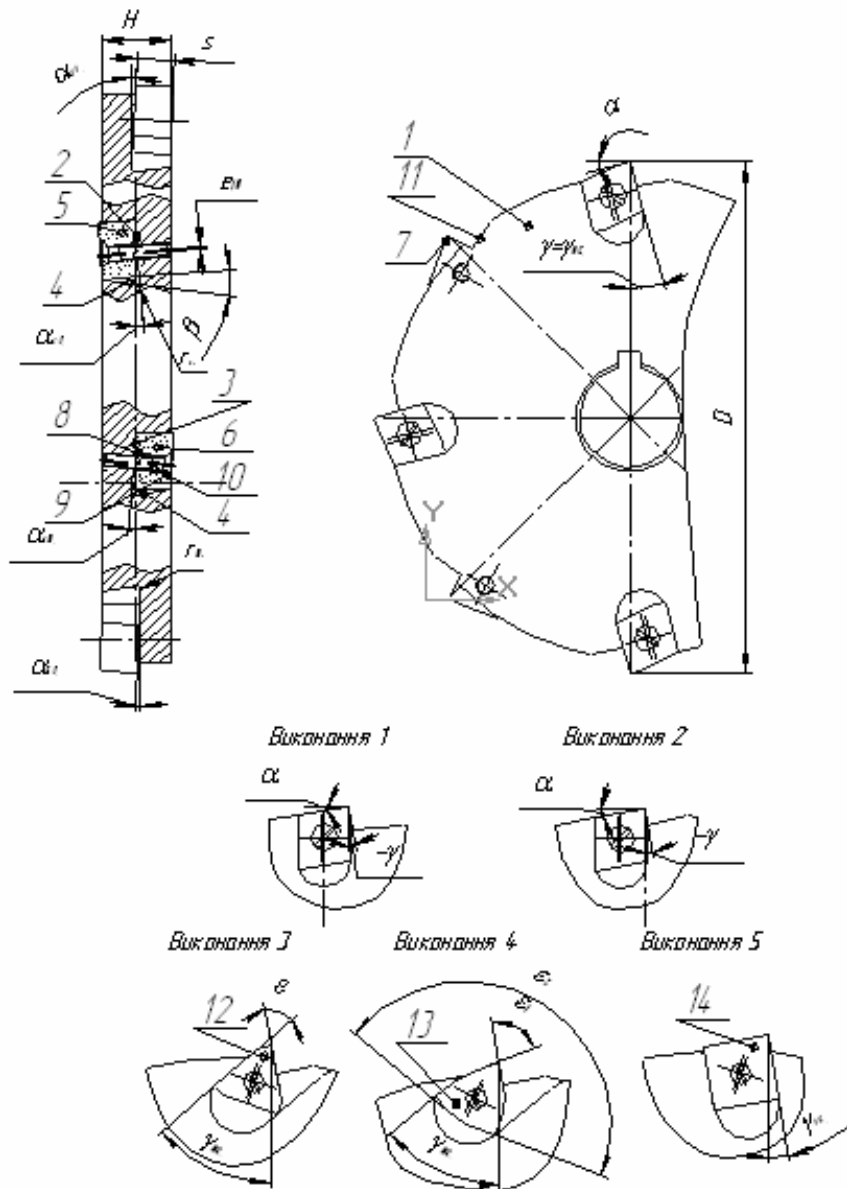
Предлагаемая конструкция сборной дисковой отрезной фрезы и варианты оснащения ее МНП боковой установки
